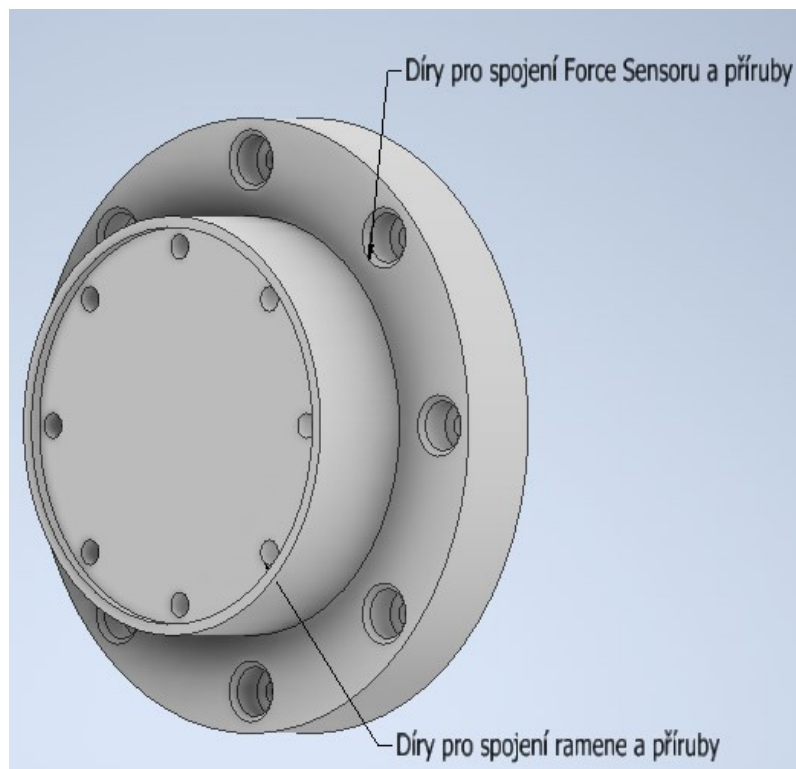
Příruba pro připojení gripperu k Force Sensoru
